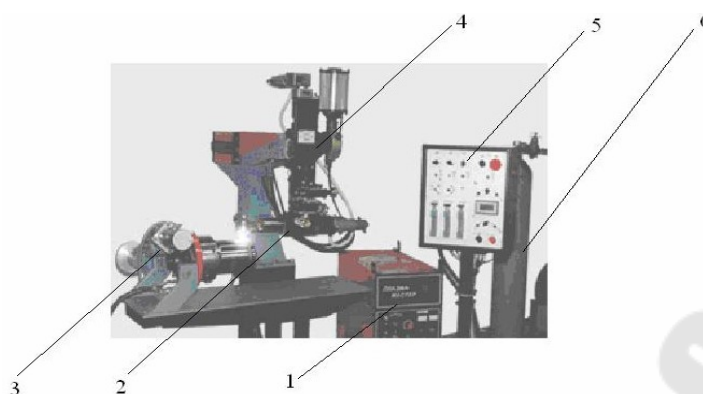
Установка для плазменно-порошковой наплавки ПМ-300В: 1 – источник питания; 2 – плазмотрон; 3 – манипулятор-вращатель; 4 – механизм регулировки плазмотрона и подачи порошка; 5 – пульт управления; 6 – баллон с аргоном
